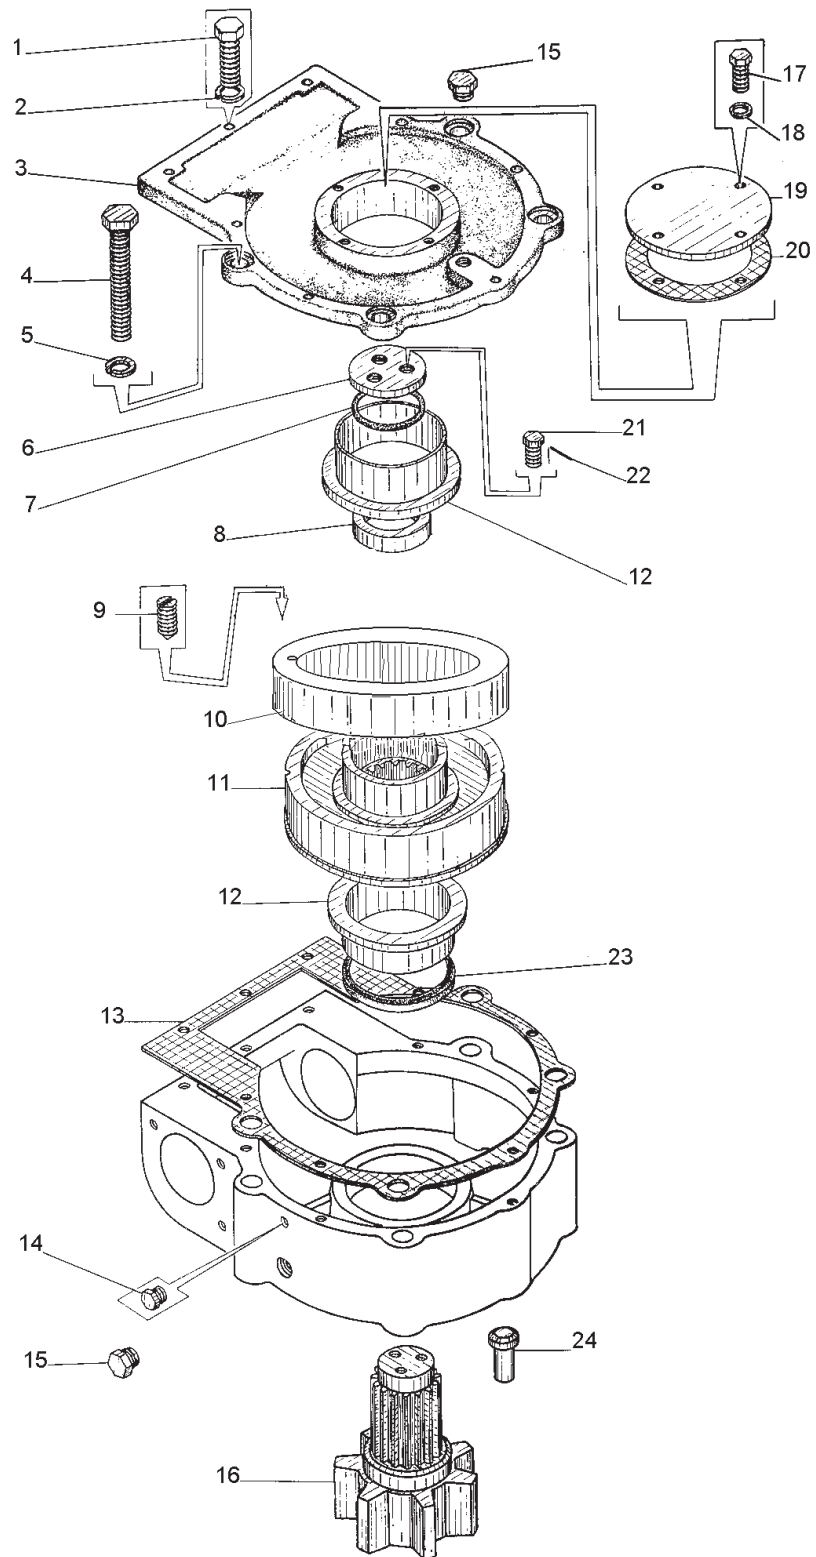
Редуктор поворота отвала (ДЗ-98.29.00.000)
